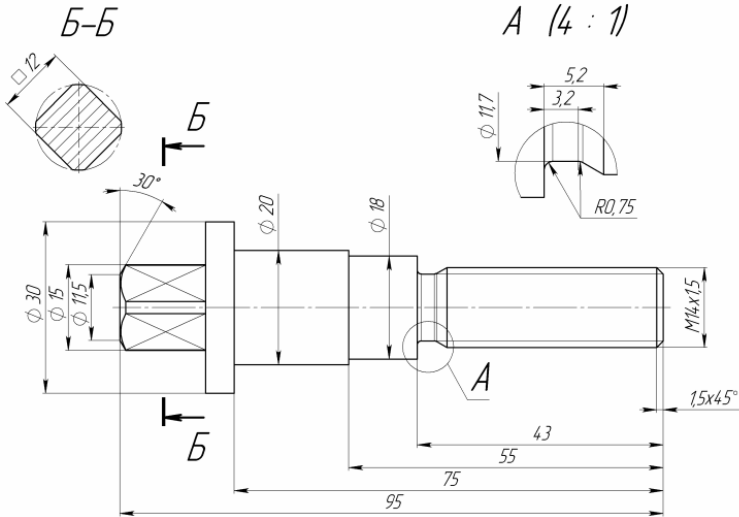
Нанесення розмірів для виготовлення валика
